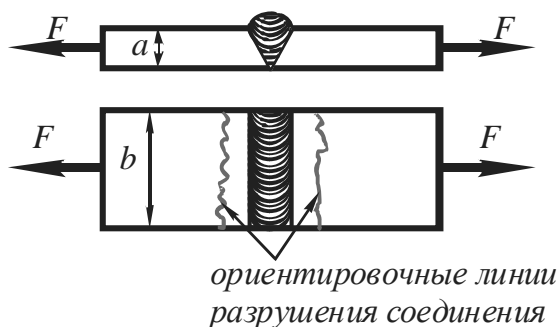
Схема стыкового сварного шва, нагруженного растягивающей (сжимающей) силой
